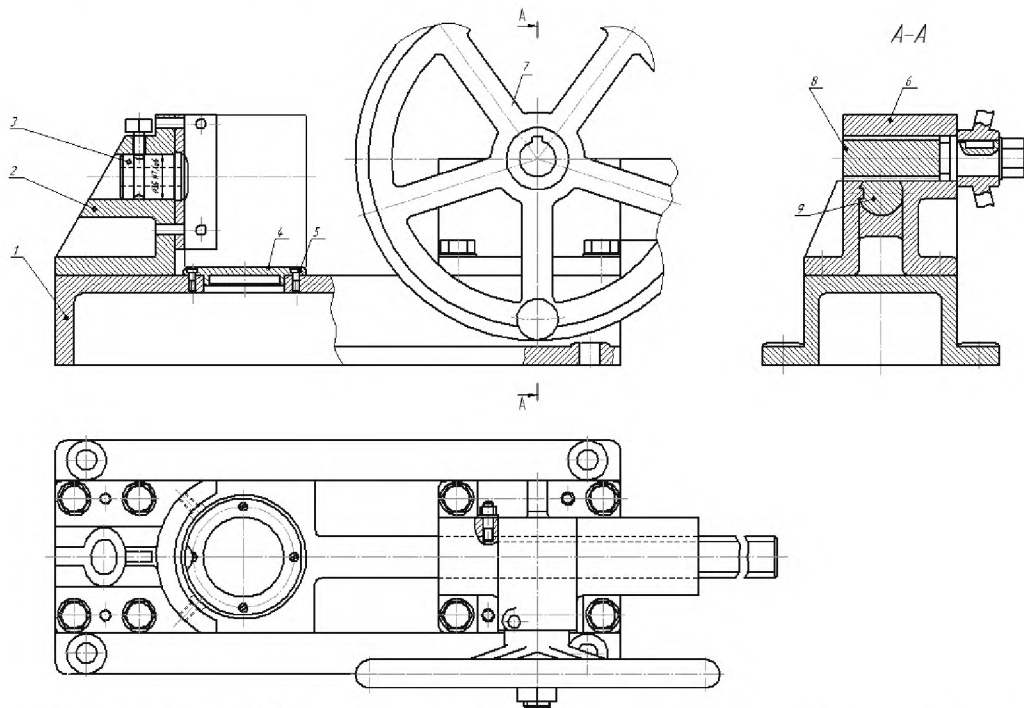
Приспособление для запрессовки и выпрессовки поршневого пальца
